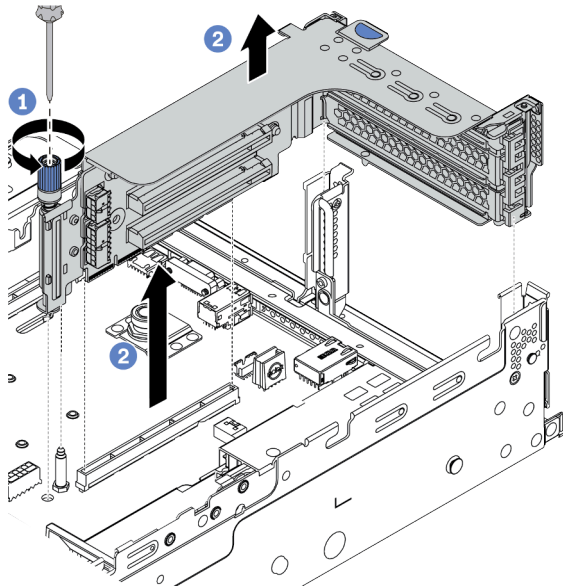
Rimozione dell'assieme verticale 1/2 (staffa a tre slot)
